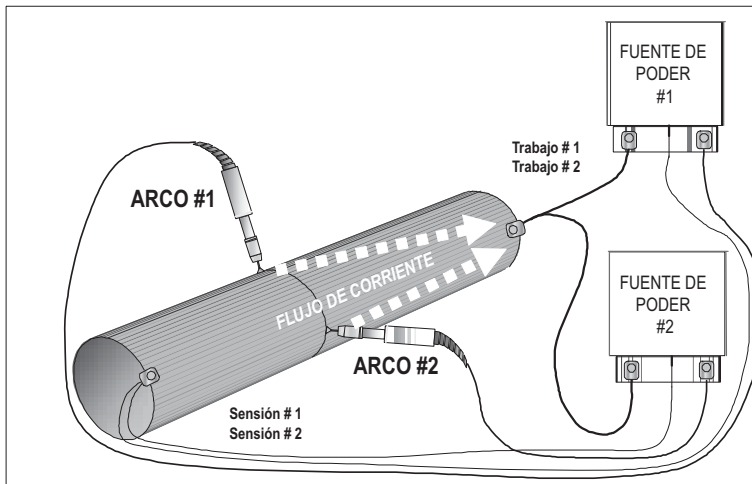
SOLDADURAS CIRCUNFERENCIALES MULTIARCO
